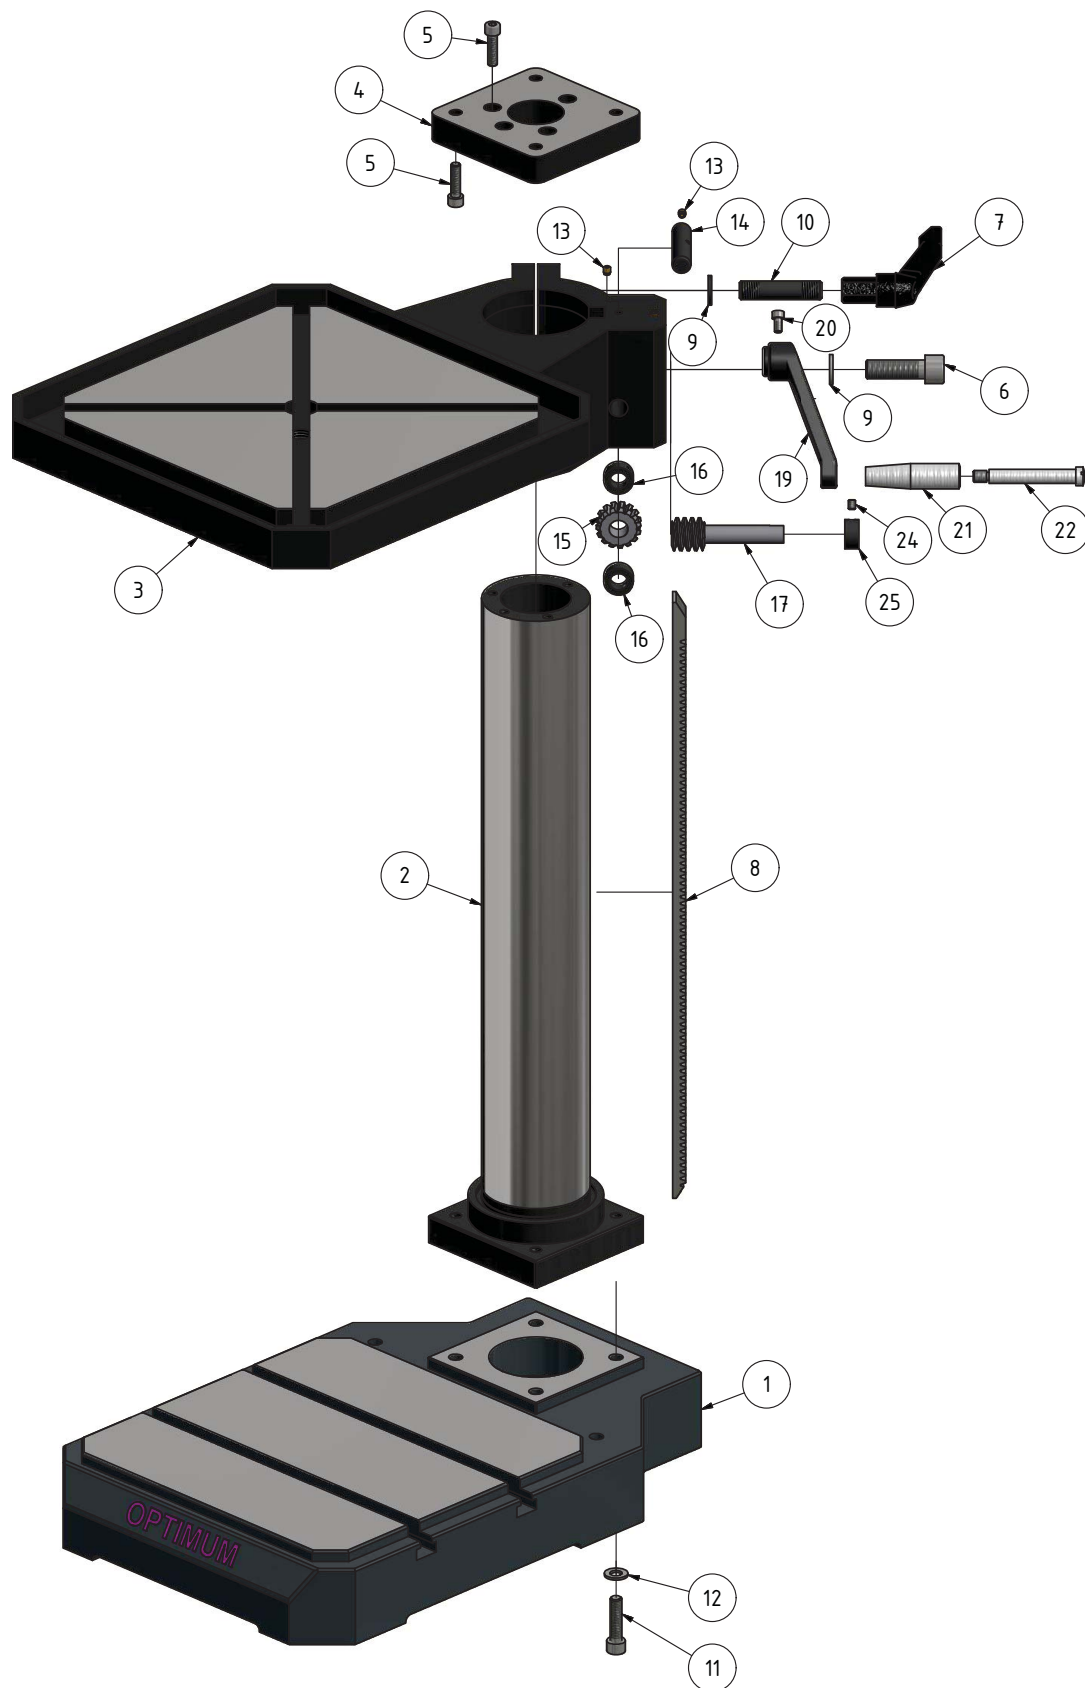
Bohrtisch - Drilling table - DH 26 GT
